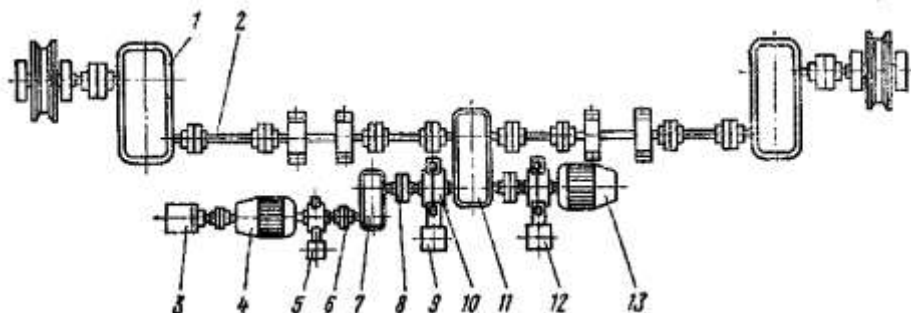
Схема двухскоростного привода механизма передвижения крана
